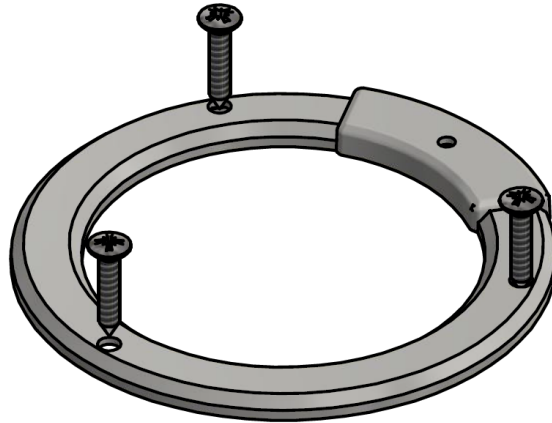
Vista isométrica de la tapa superior más tornillo autoroscante M3.5x22
